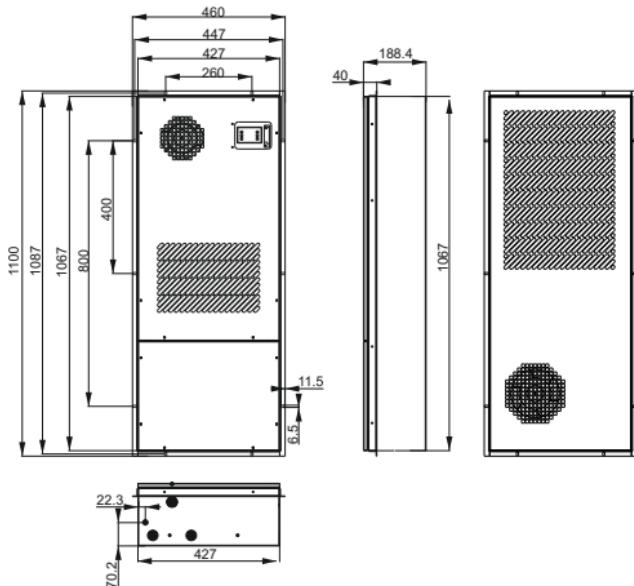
Внешний вид и габаритные размеры модели СМ-2000-230 / Figure 4 – Appearance and overall dimensions of CM-2000-230 version
